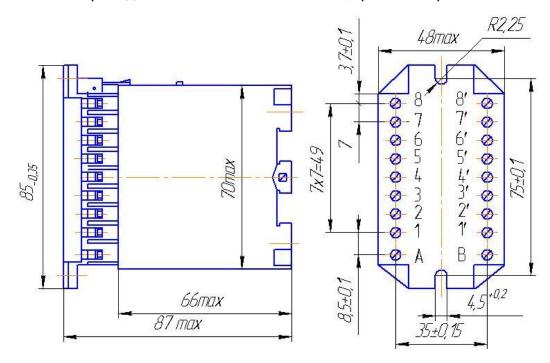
Габаритные, установочные, присоединительные размеры реле с колодкой контактной разъемной с задним присоединением внешних проводников винтовыми зажимами, крепление реле винтом.
